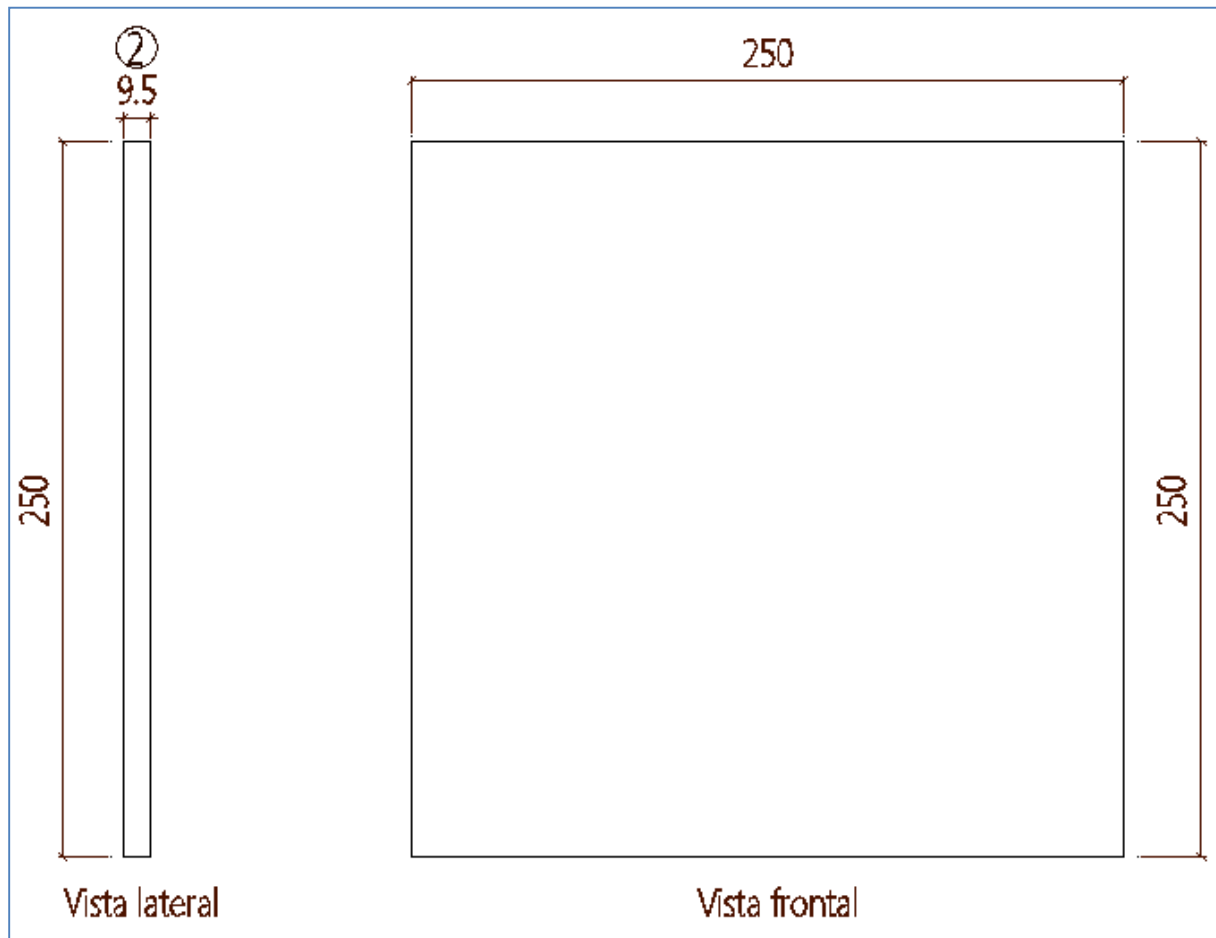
Detalle despiece pieza No.2 modelo 2 tensión.
